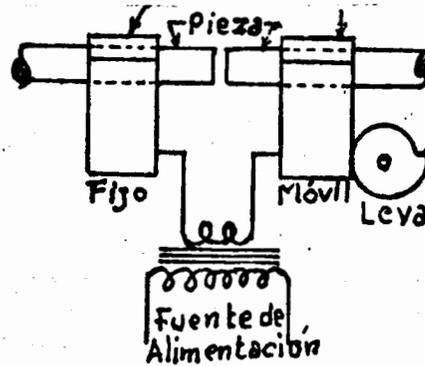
PRINCIPIO DE LA SOLDADURA POR CHISPAS.
